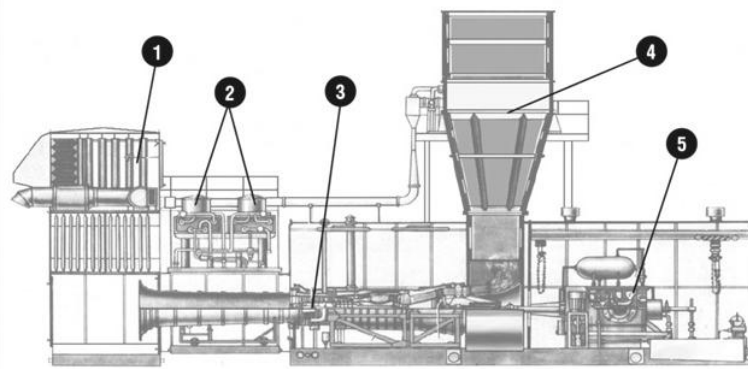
Устройство газоперекачивающего агрегата: 1 – входное воздухоочистительное устройство; 2 – масляные радиаторы; 3 – привод; 4 – выхлопное устройство; 5 – нагнетатель газа
